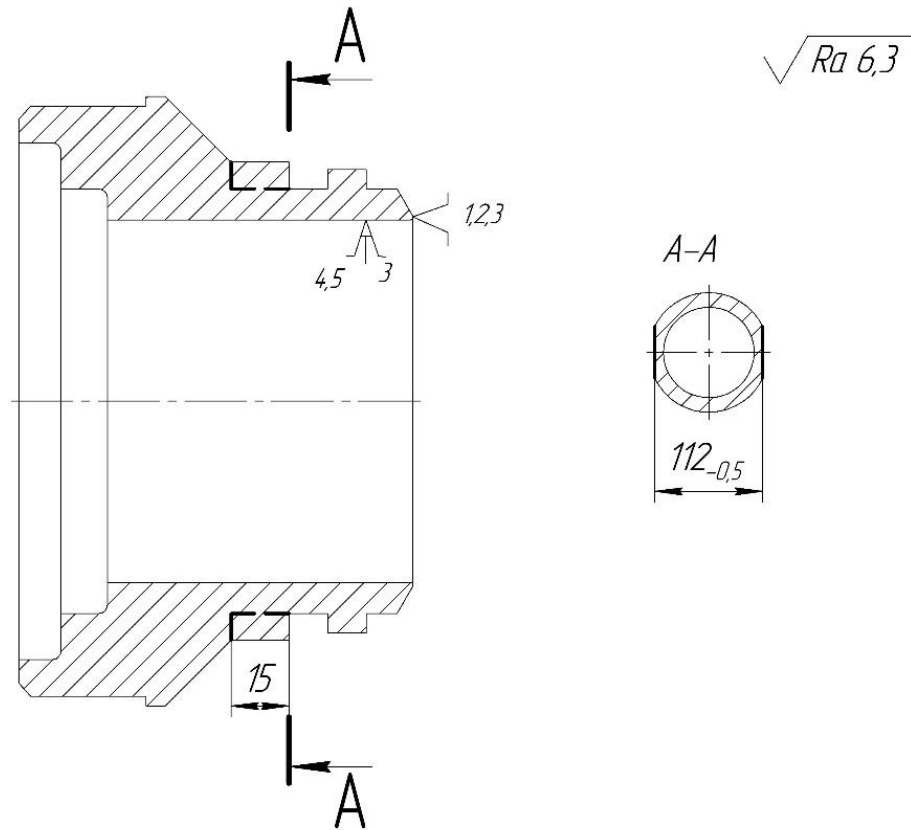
Схема базування заготовки на операції комплексній з ЧПК 015, позиція 2
